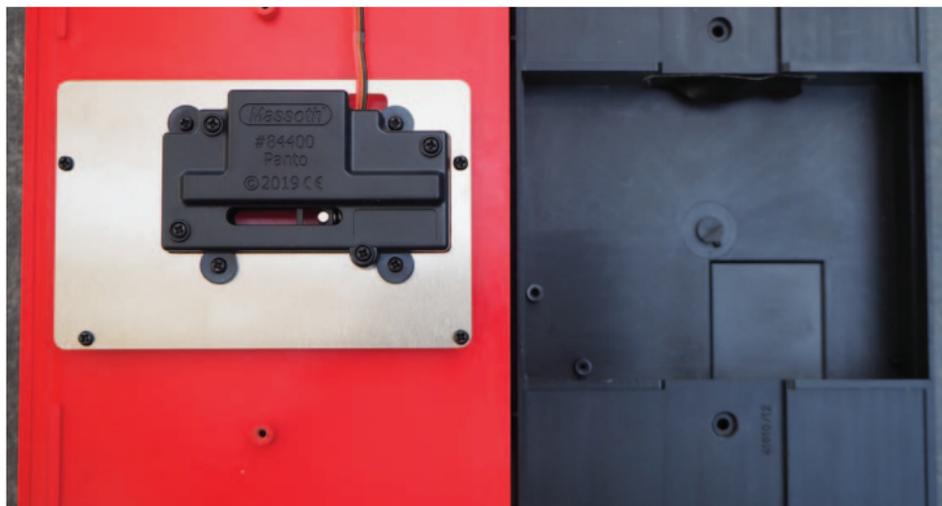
Antrieb mit Montageplatte im Wagenkasten montiert.
